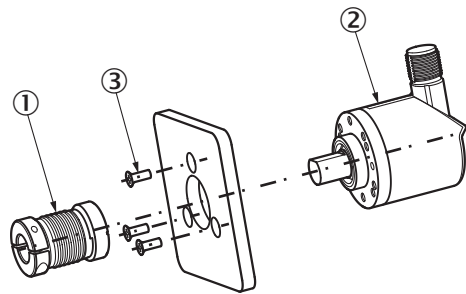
Anbau über flanschseitige Gewindebohrung
